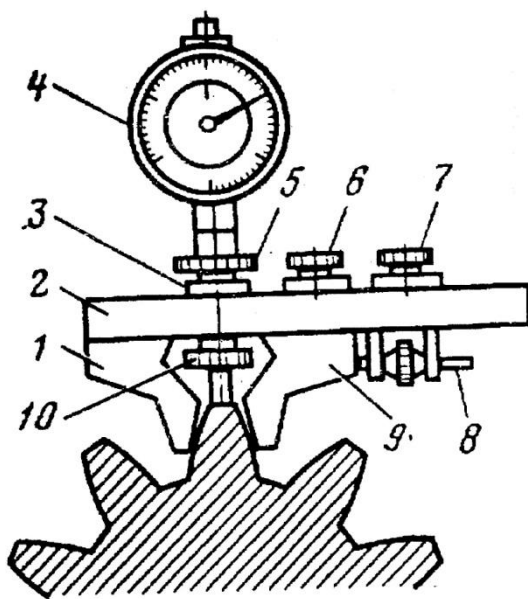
Загальний вигляд розробленого пристосування для
